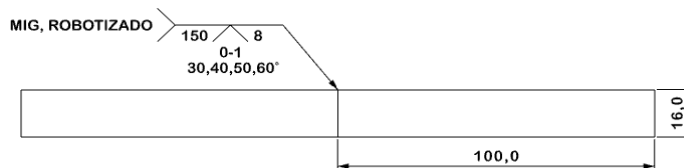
Diseño de unión para el soldeo de placa AISI 1018 con GMAW robotizado.
